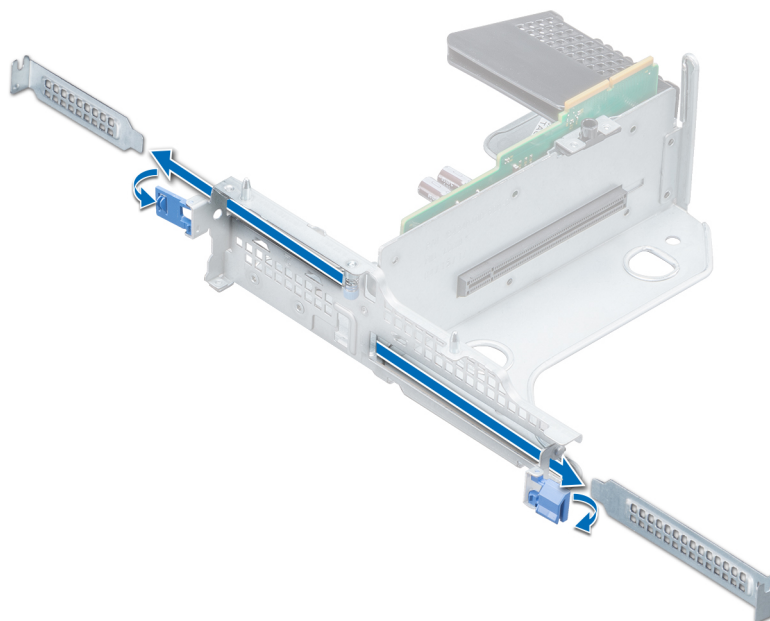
Entfernen des Abdeckblechs für Butterfly Riser
